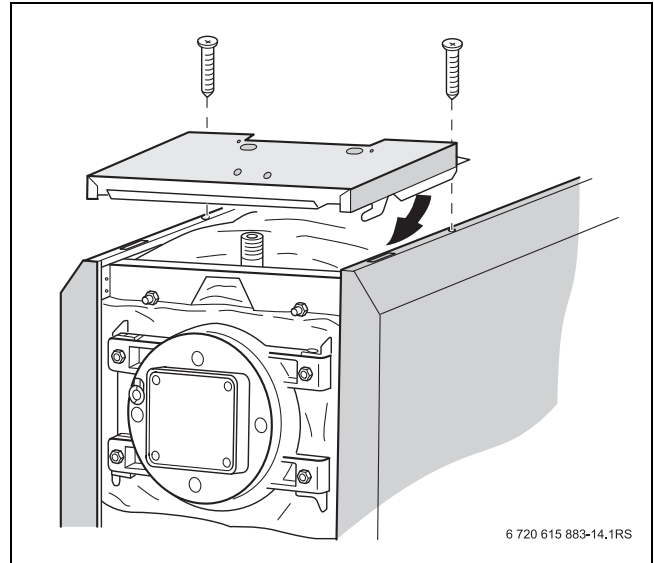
Položení dílů krytu kotle - principiální zobrazení
